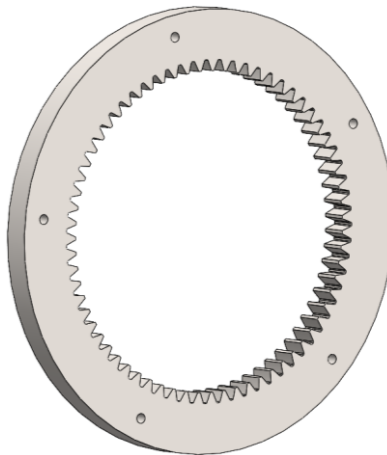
Modelo geométrico CAD 3D del engrane anillo.
